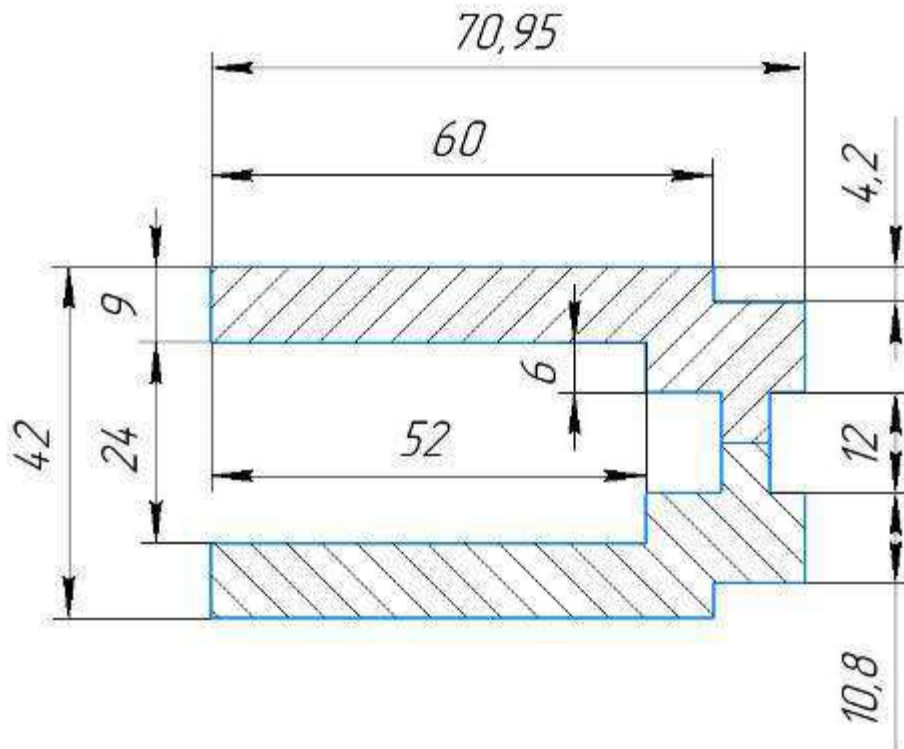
Ескіз заготовки деталі перед кінцевою обробкою
